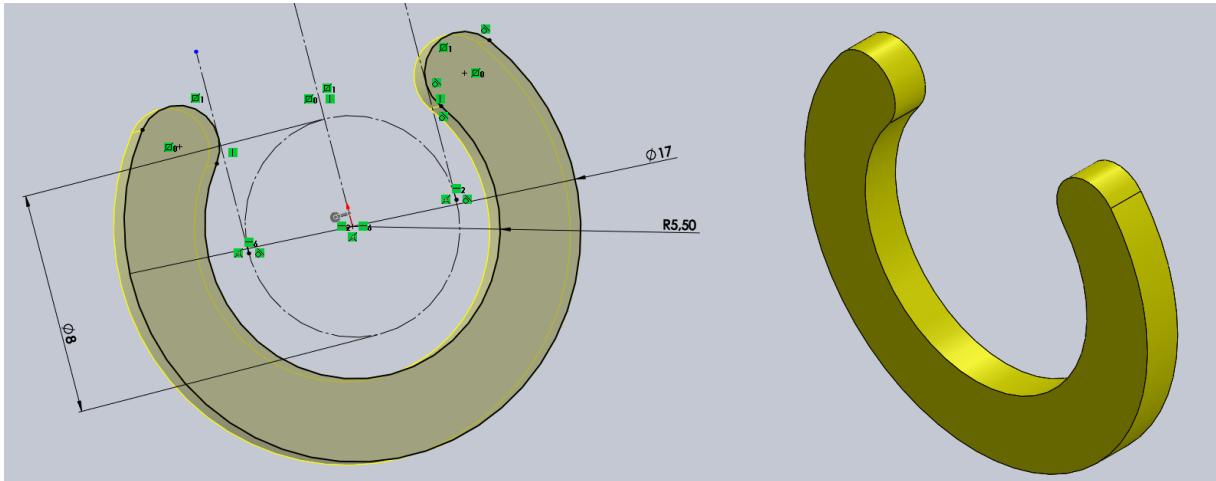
A la izquierda: extrusión desde su croquis a una cota de 1.5mm. A la derecha: perspectiva de la pieza terminada.
